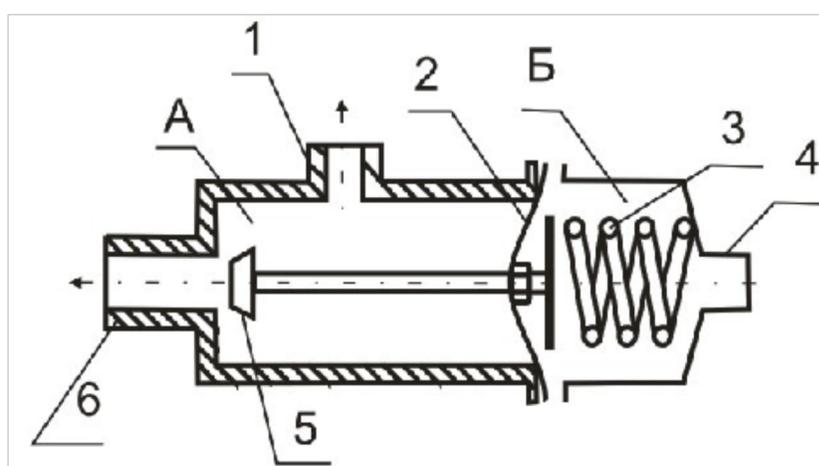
Регулятор давления топлива: 1 – входной патрубок топлива; 2 – диафрагма; 3 – пружина; 4 – вакуумный патрубок; 5 – клапаны; 6 – патрубок отвода топлива в бак.
